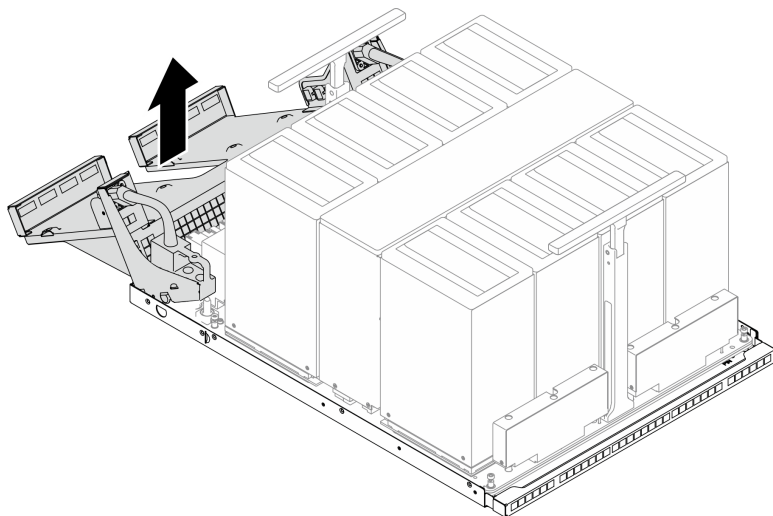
Entfernen des OSFP-Trägerrahmens
